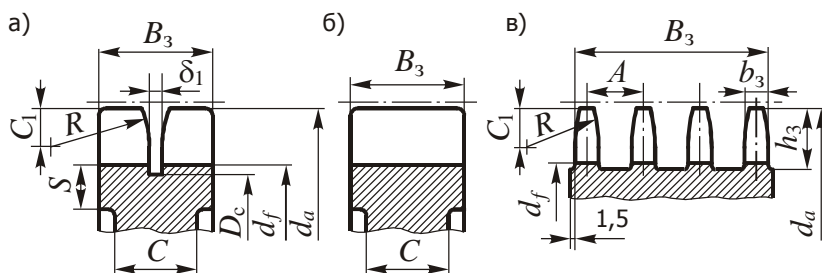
Венцы звездочек зубчатых цепных передач: а – для цепи типа 1 с прорезью под внутренние направляющие пластины; б – для цепи типа 1 с боковыми направляющими пластинами; в – для цепи типа 2
